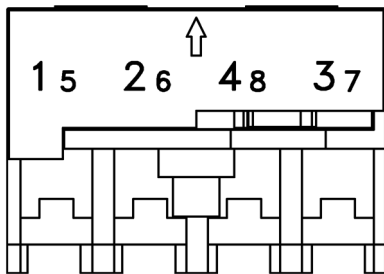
Kennzeichnung der Steckpositionen auf dem 4-fach Halter
